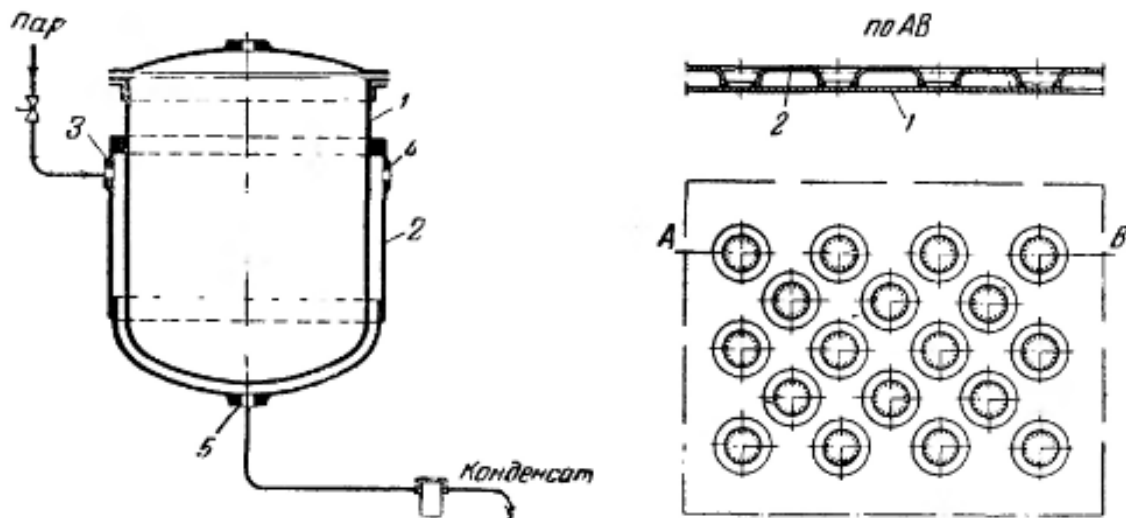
Схема устройства паровой рубашки: 1—корпус аппарата; 2—рубашка; 3—5—штуцеры
